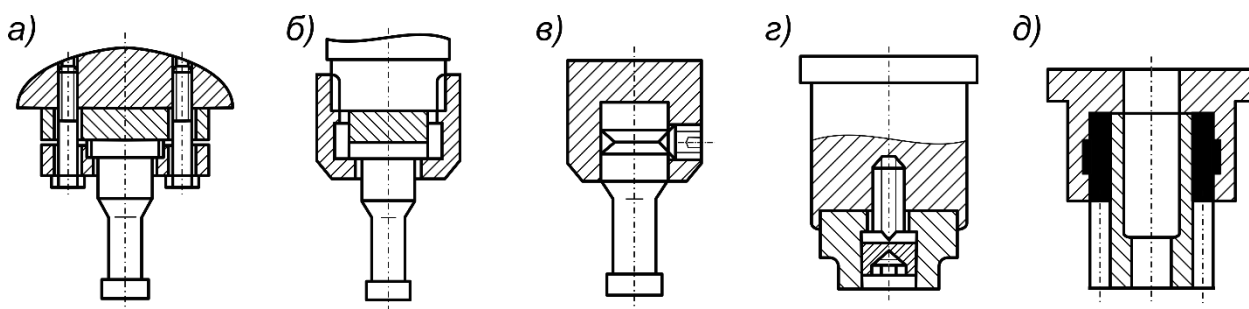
Схемы крепления пуансонов: а, б – фланцевое крепление пуансонодержателями; в – канавочное крепление винтами или шариками; г – сквозное крепление болтами; д – крепление заливкой пластмассы
